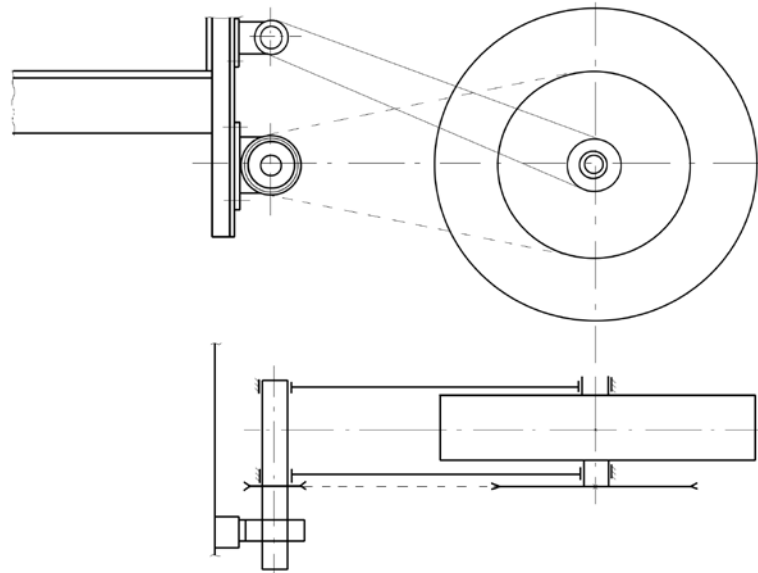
Схема компоновки крепления индивидуального колеса к раме разбрасывателя
